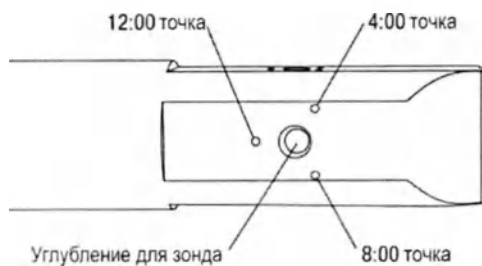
Точки калибровки фиксатора руки-манипулятора.
